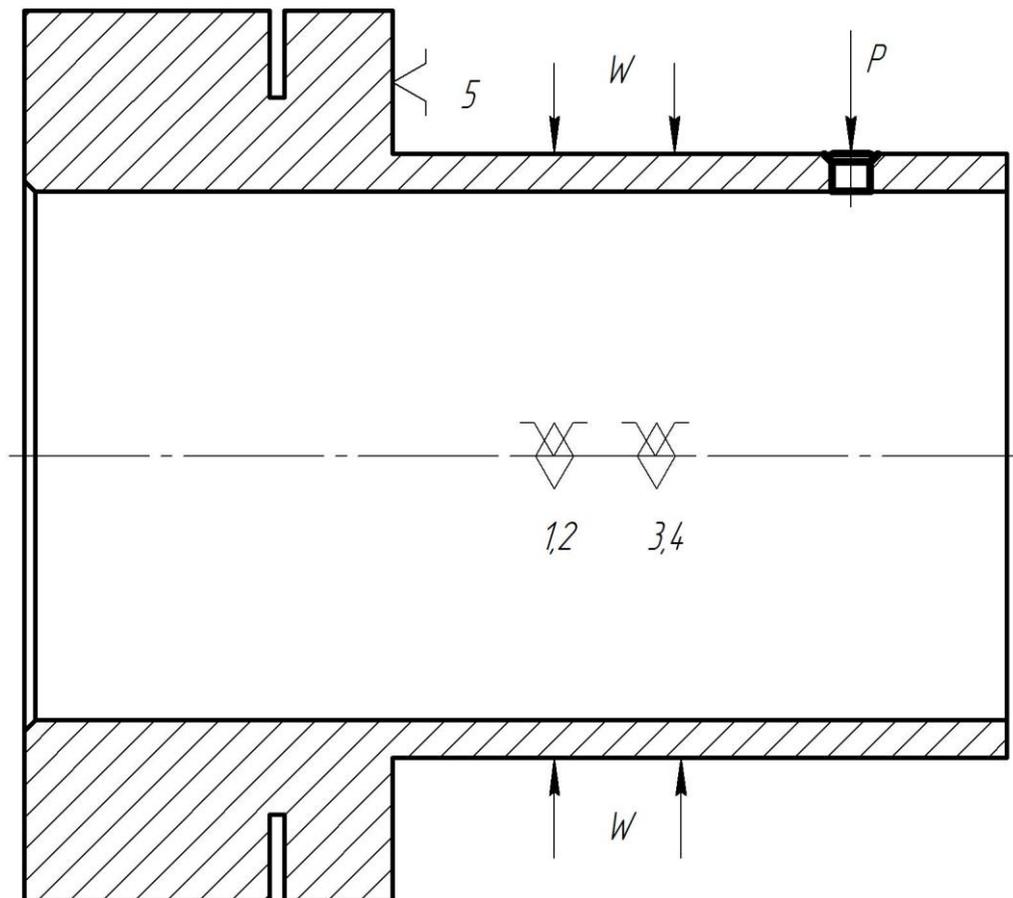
Схема базирования заготовки в приспособлении с указанием мест приложения силы зажима
